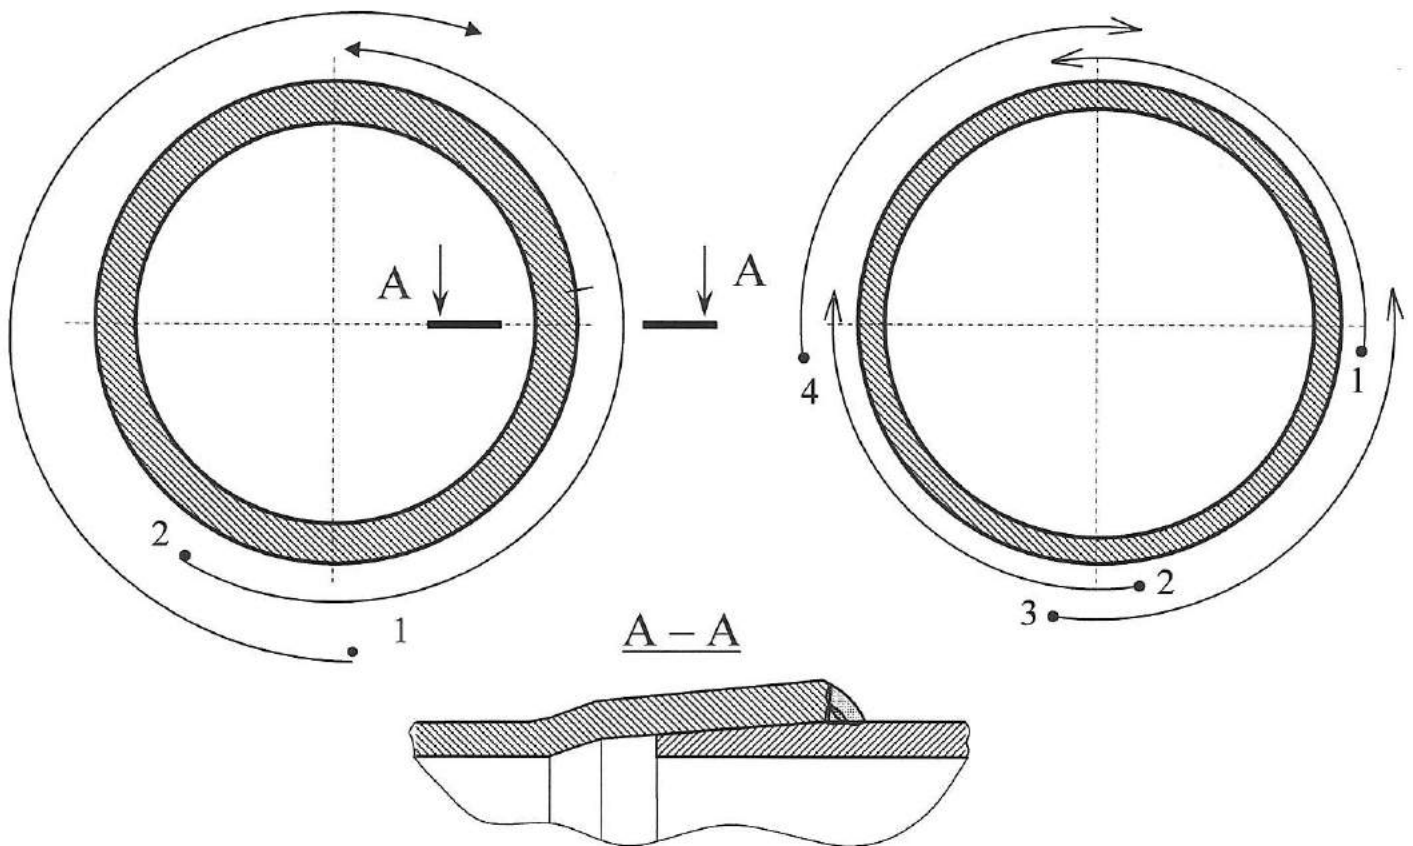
Порядок наложения слоев при сварке кольцевых швов (стыковых и угловых):
